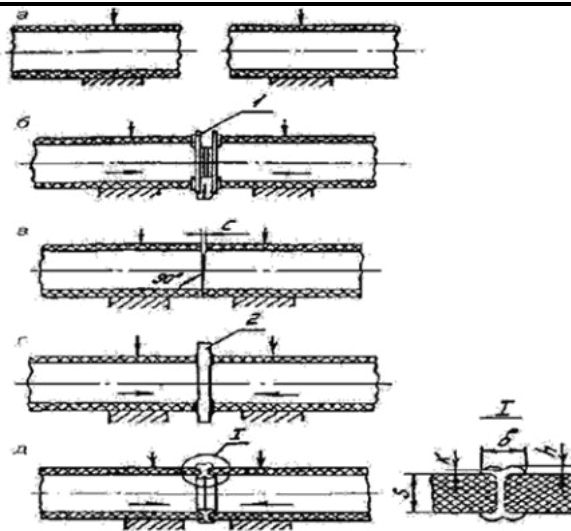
Последовательность процесса сборки и стыковой сварки труб контактным нагревом: а - центровка и закрепление в зажимах сварочной машины концов свариваемых труб; б - механическая обработка торцов труб с помощью торцовки (1); в - проверка точности совпадения торцов по величине зазора (с); г - нагрев и оплавление свариваемых поверхностей нагретым инструментом (2); д - осадка стыка.
